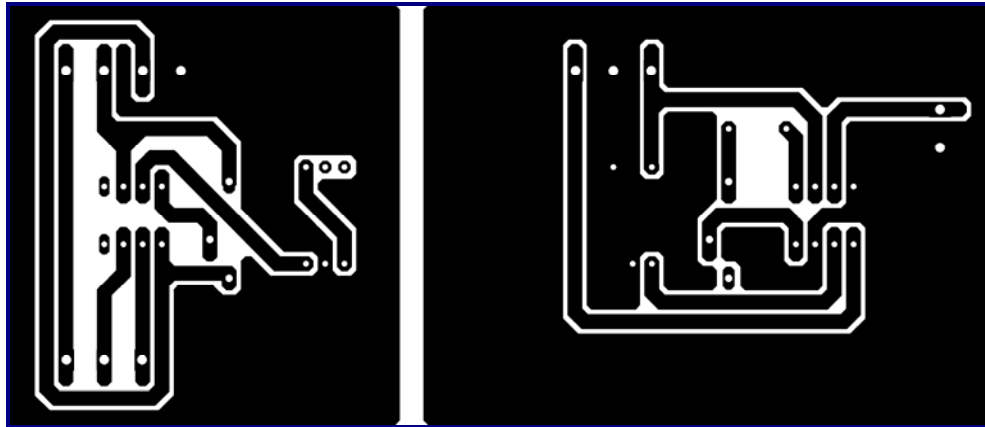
PCB de la Etapa de Acondicionamiento de la Señal del Sensor y Aislamiento.
